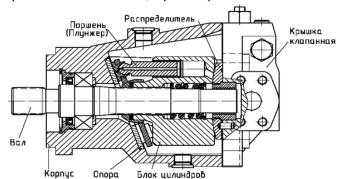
Гидромотор 406.0 с противоположным расположением рабочих
